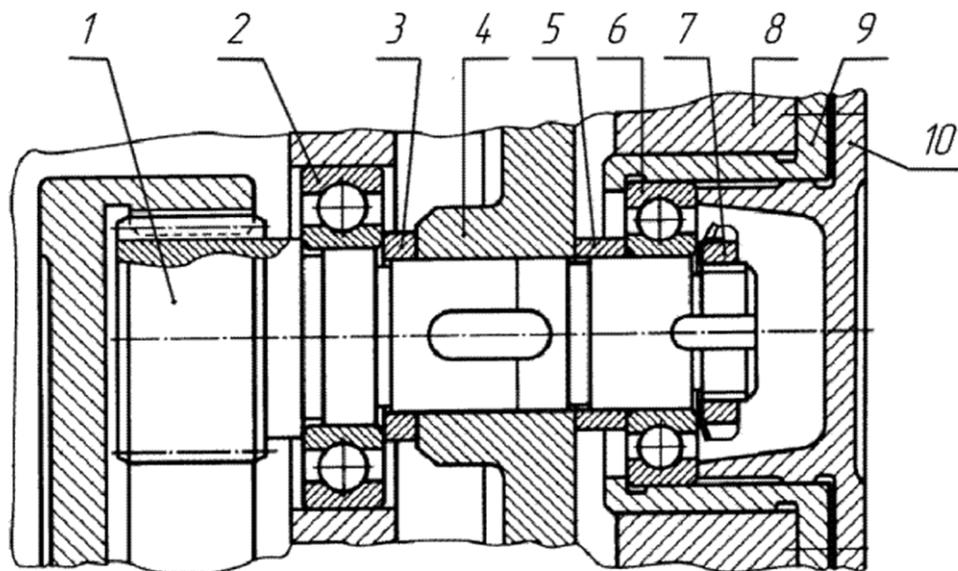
Промежуточный вал цилиндрического редуктора внутреннего зацепления:
